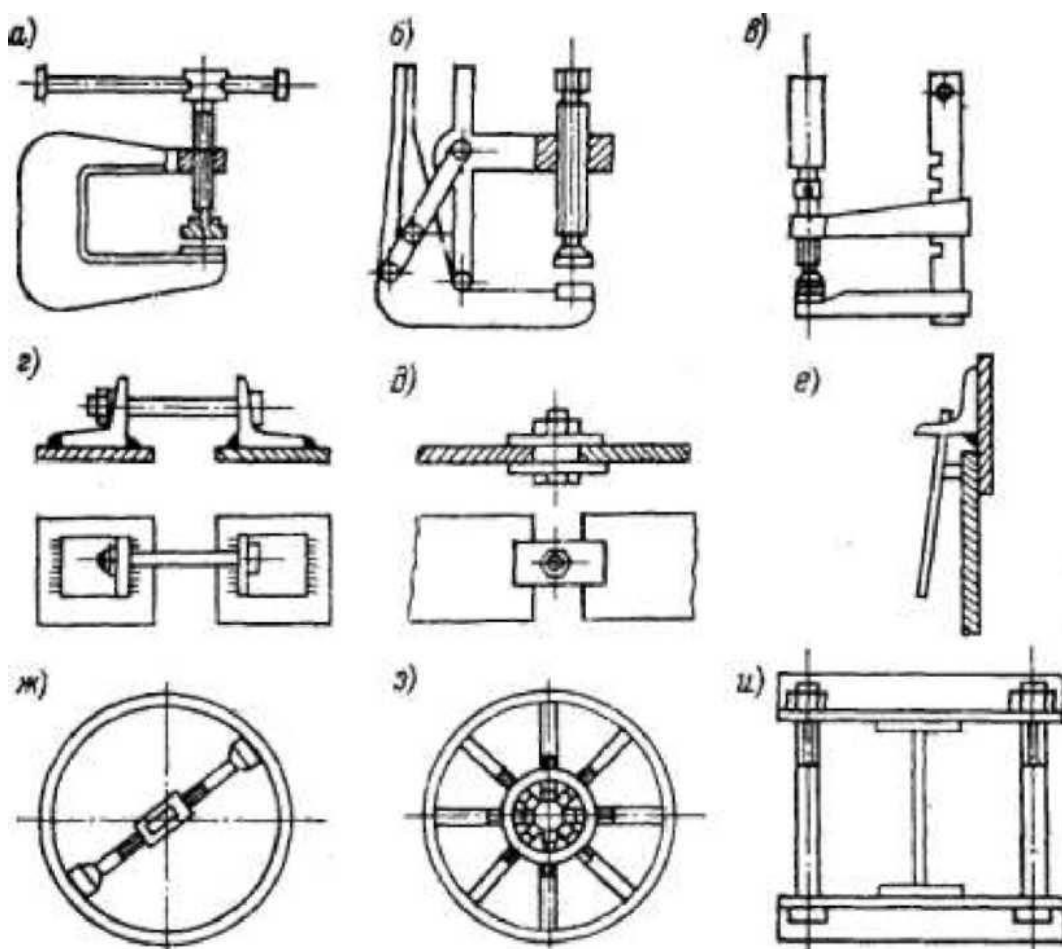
Универсальные приспособления для сборки: *а, б, в* – струбцины; *г, д* – стяжные устройства; *е* – прижим рычажный; *ж, з* – распорки (стяжки) винтовые; *и* – стяжное приспособление (хомут)
